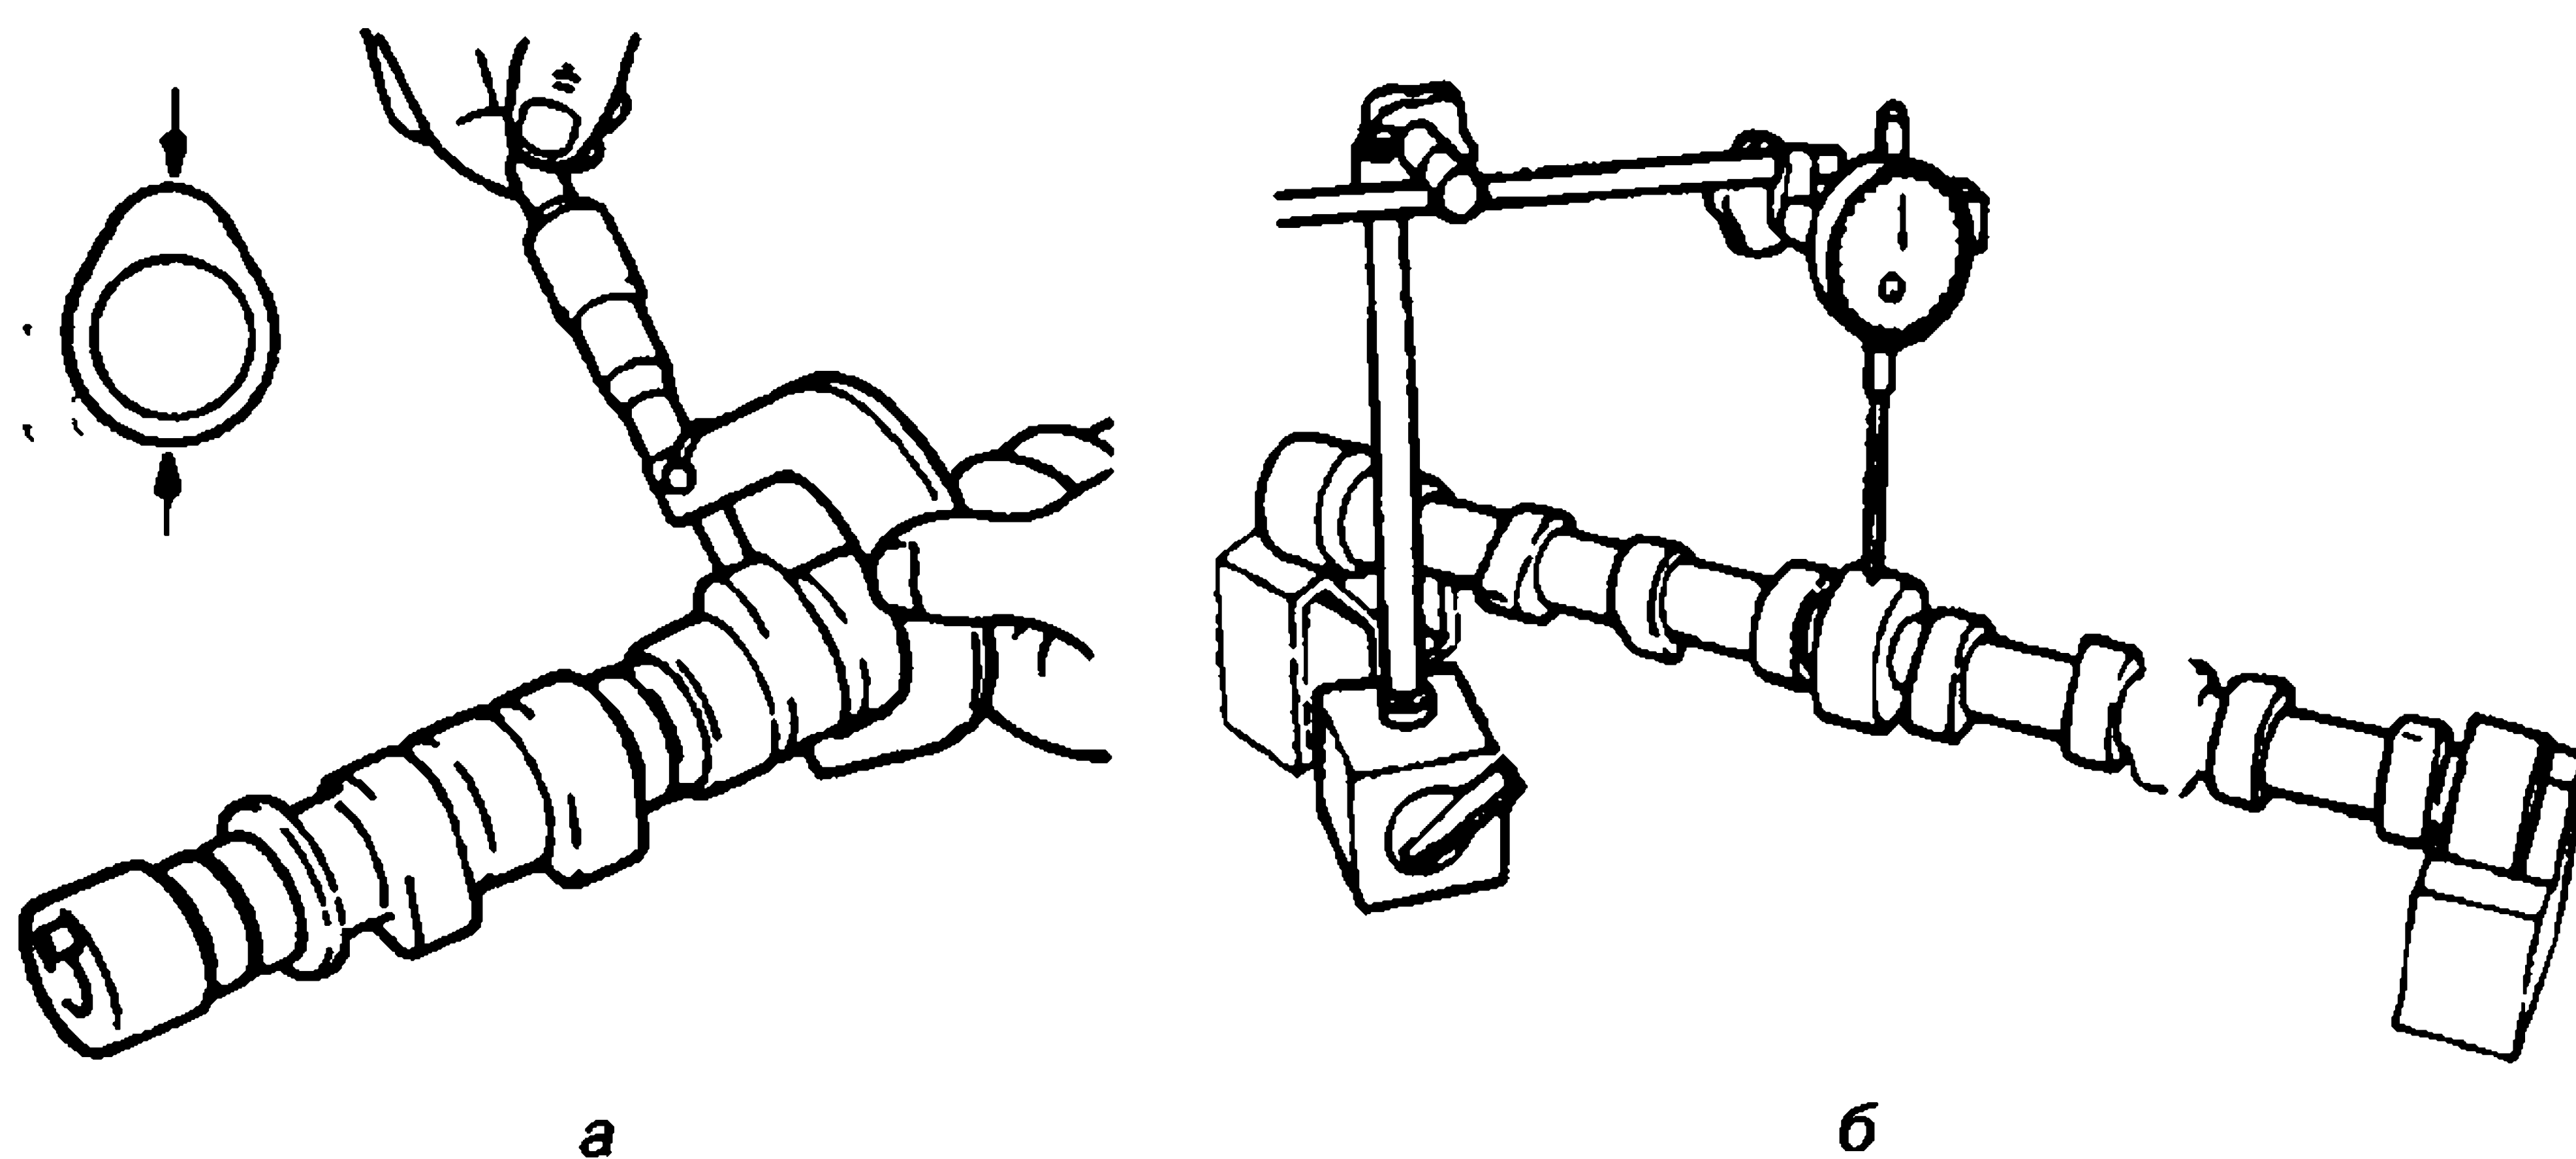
Проверка размеров (а) и биения (б) распределительного вала
